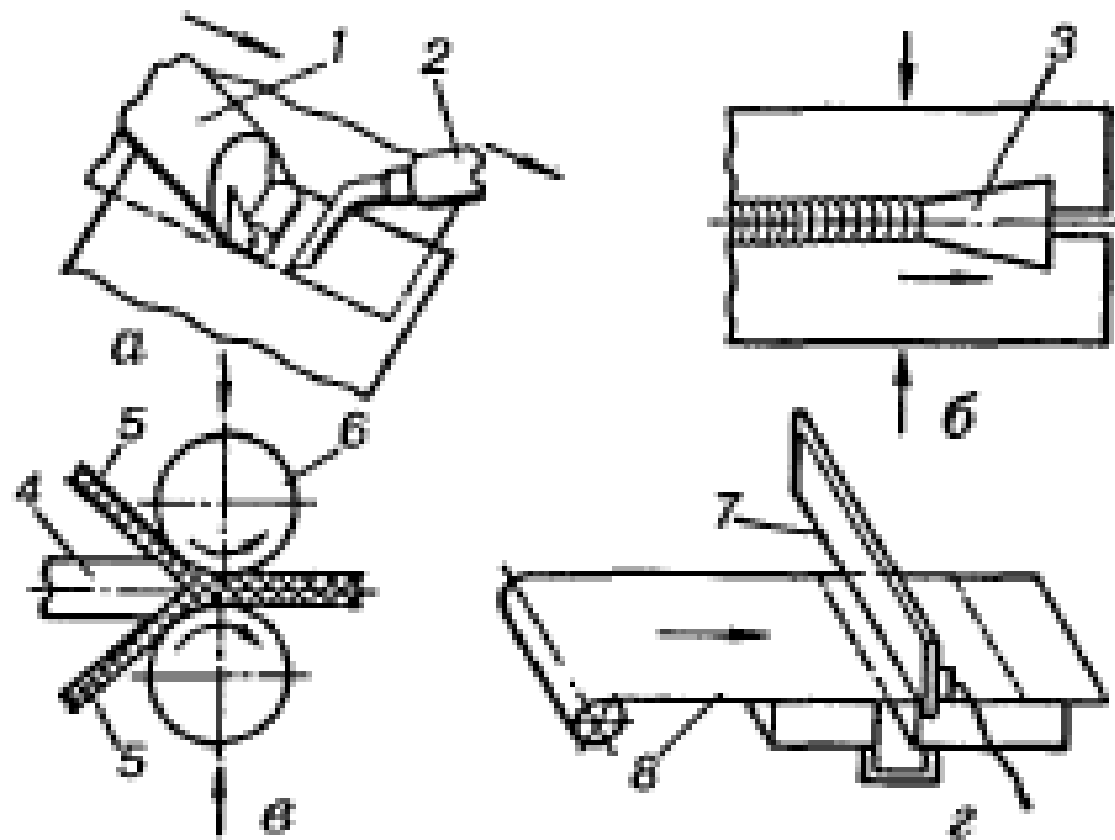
Способи зварювання пластмас нагрітим інструментом
